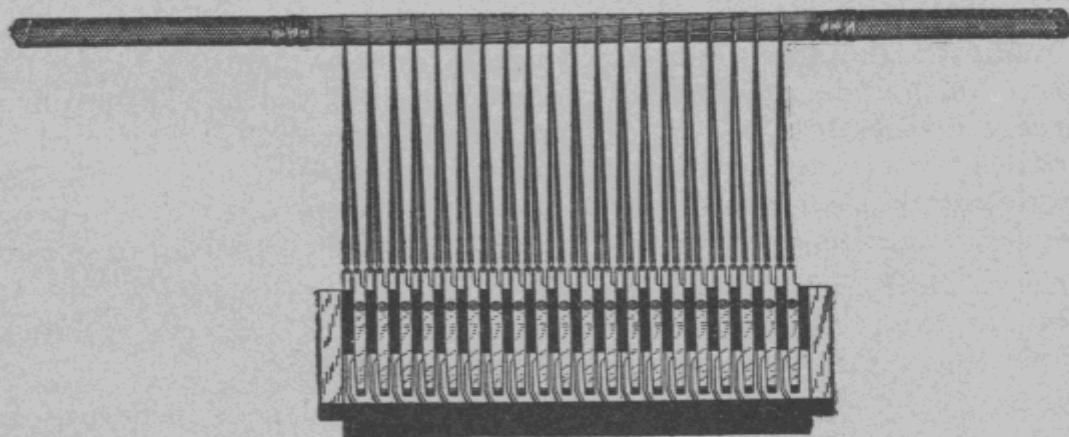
Soudage des câbles sur une réglette de jacks.
